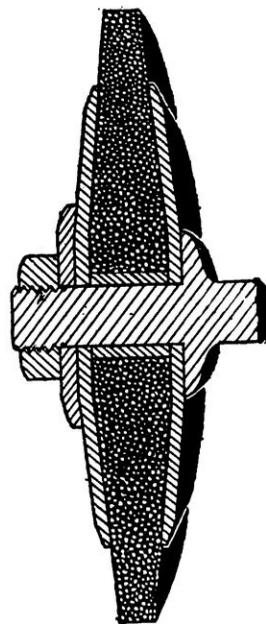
MEULE POUR L'USINAGE DES PIÈCES MÉCANIQUES
